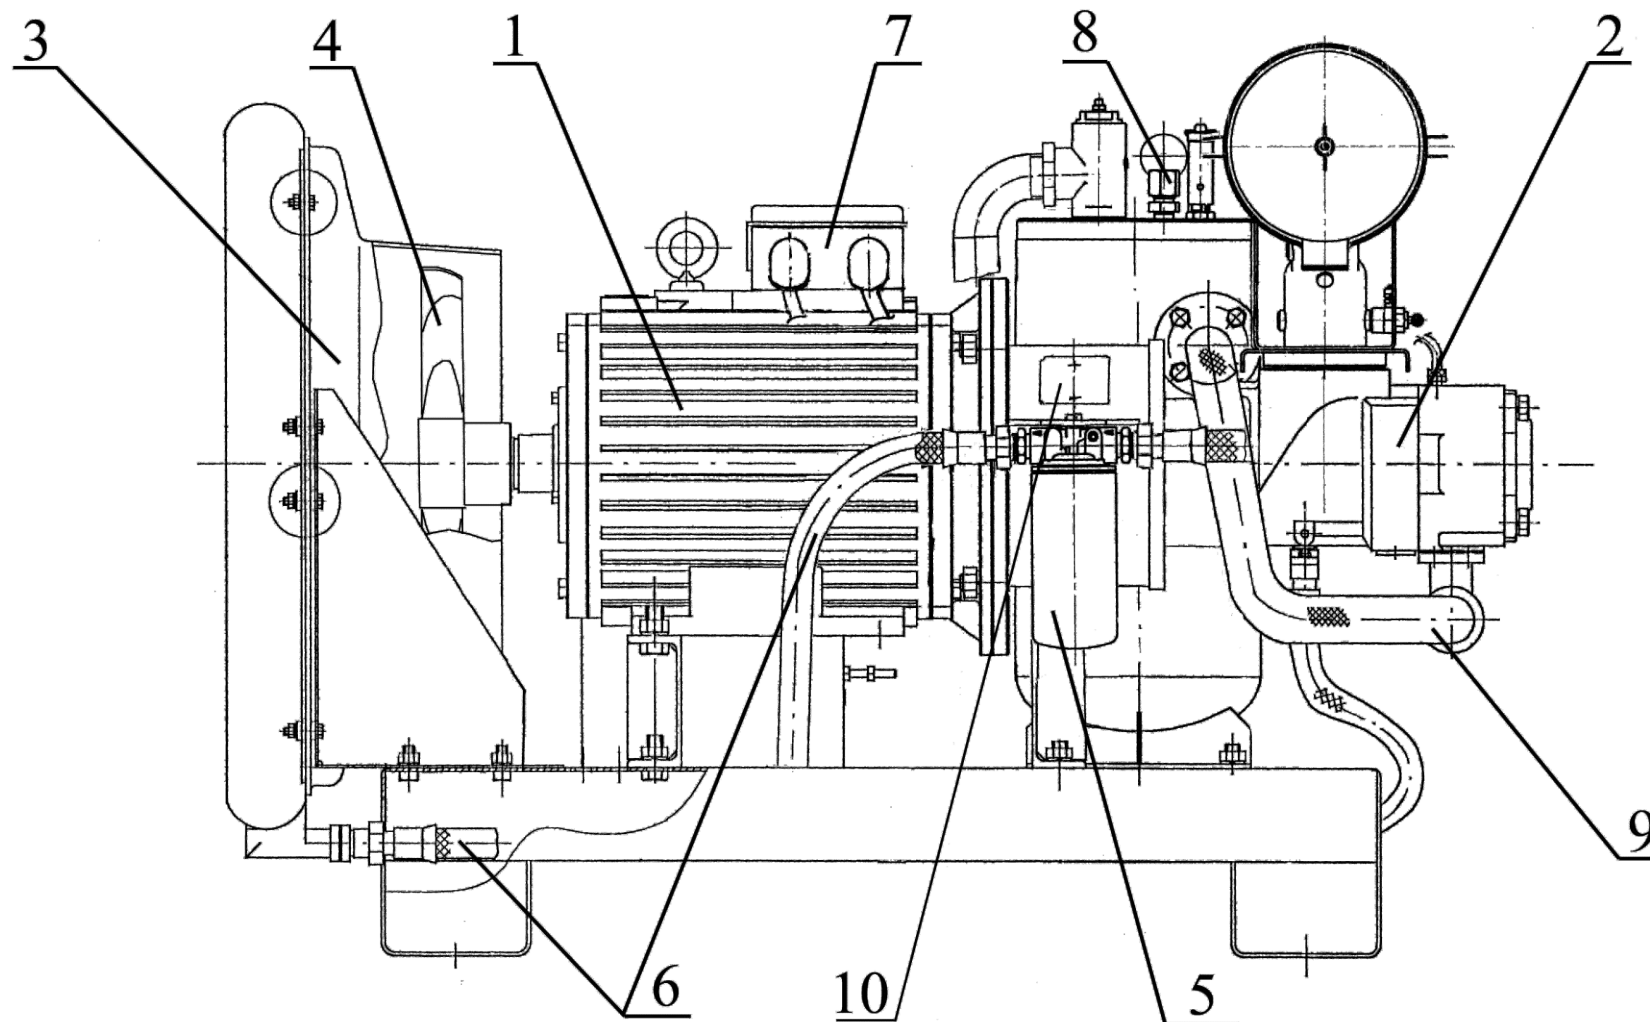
Габаритный чертеж компрессорных станций ЗИФ-СВЭЗ/0,7 (АРМ19-22-01)
